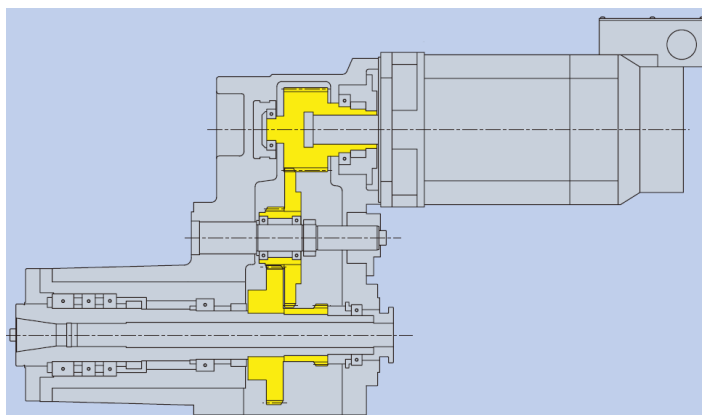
Шпиндель центровой BIG PLUS
